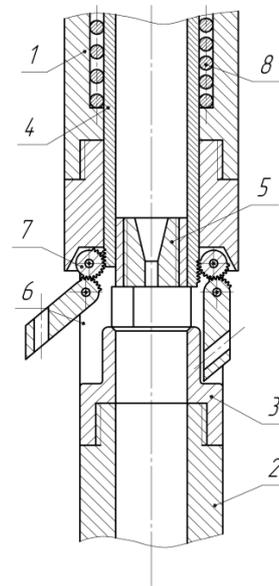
ЗУ со складывающимися лепестками шестеренчатого типа:
